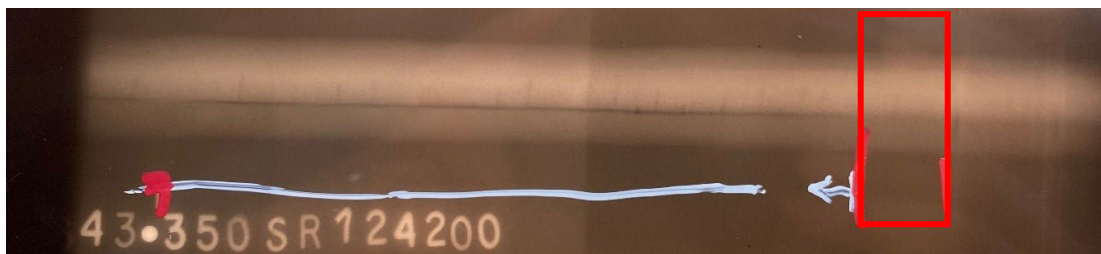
Placa radiográfica de la soldadura de referencia 124200.
